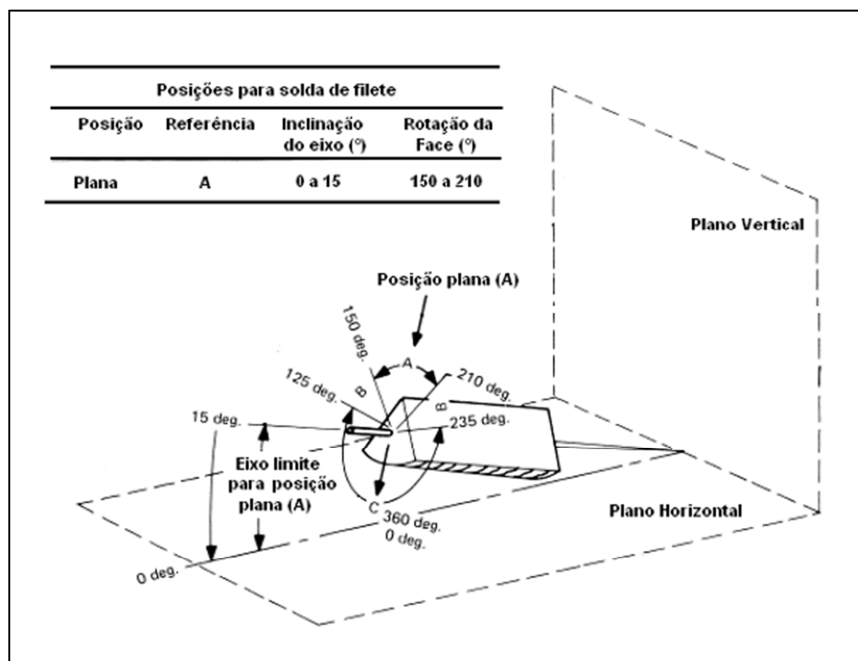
Posições de soldagem (Adaptado de UFTPR, 2006).
